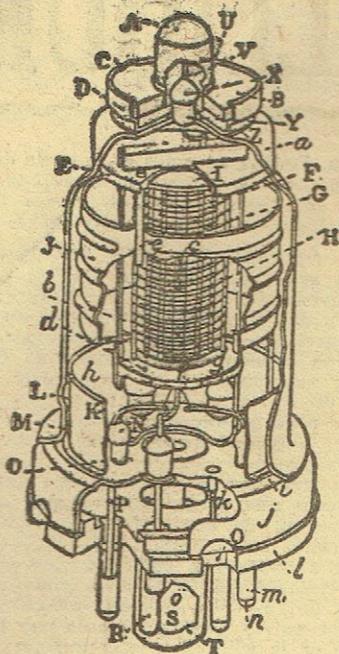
Coupe d'une lampe métallique (Mazda) : A, soudure; — B, isolant supérieur; — C, bord roulé; — D, chapeau d'ampoule; — E, disque écran; — F, grille n° 1; — G, grille n° 2; — H, grille n° 3; — I, pont de mica pour centrage supérieur; — J, anode; — K, support de montage; — L, pastille de « getter »; — M, collier écran; — N, perle de scellement; — O, œillet de fer-nickel; — P, conducteur; — Q, cran de sertissage du culot; — R, ergot-guide du culot; — S, pincement du queueux; — T, guide central du culot; — U, coiffe; — V, conducteur de grille; — X, perle de scellement; — Y, œillet de fer-nickel; — Z, brasure; — a, ampoule en acier; — b, cathode; — c, élément chauffant; — d, substance émissive; — e, écran; — f, connexions du filament; — g, grille; — h, collier écran; — i, soudure autogène sur acier; — j, platine d'acier; — k, conducteur de masse; — l, culot; — m, broche; — n, soudure; — o, queueux de pompage à la partie inférieure.
